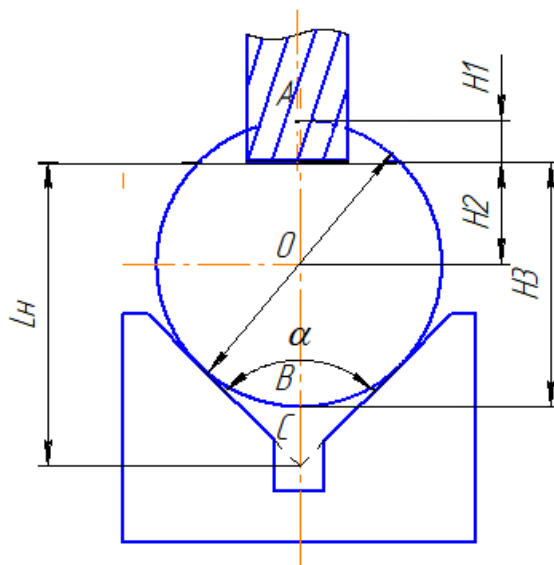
Похибка базування під час базування заготовки в призмі: L_h - розмір налагодження, D - діаметр заготовки з допуском T_d , H_i - конструкторський розмір
